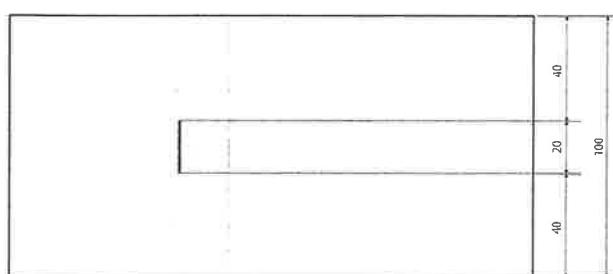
鋼板に放電加工によるスリットまたは横穴を内蔵させた試験体 (t16) の平面図
